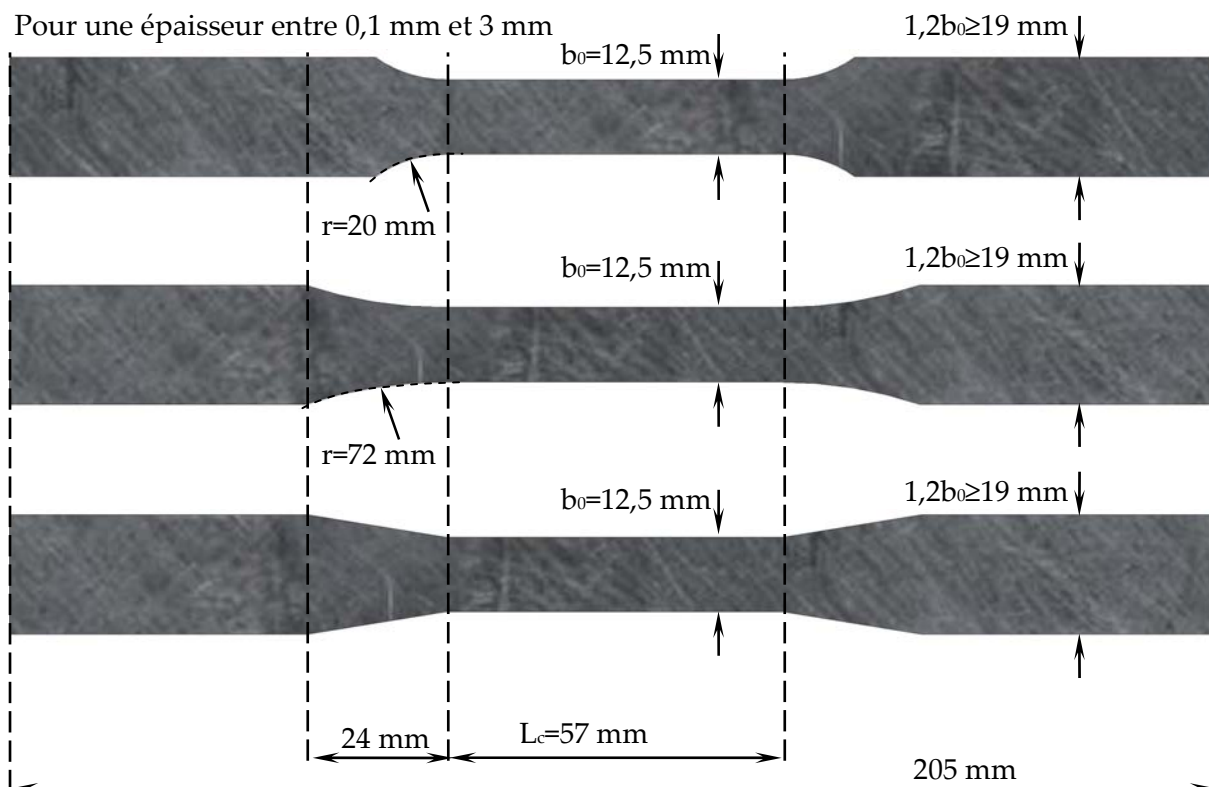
Dimensions des éprouvettes en acier pour le test des tôles.
